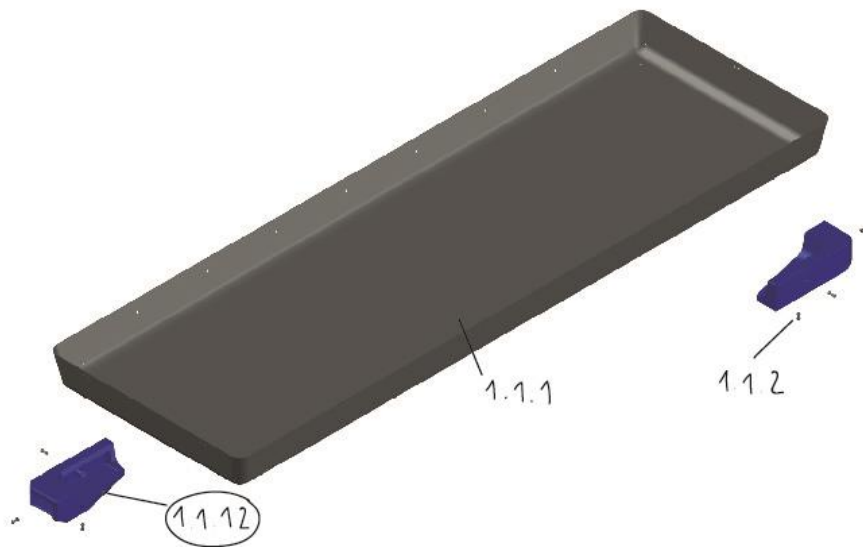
Explosionado de relaciones pieza 1.1.12
